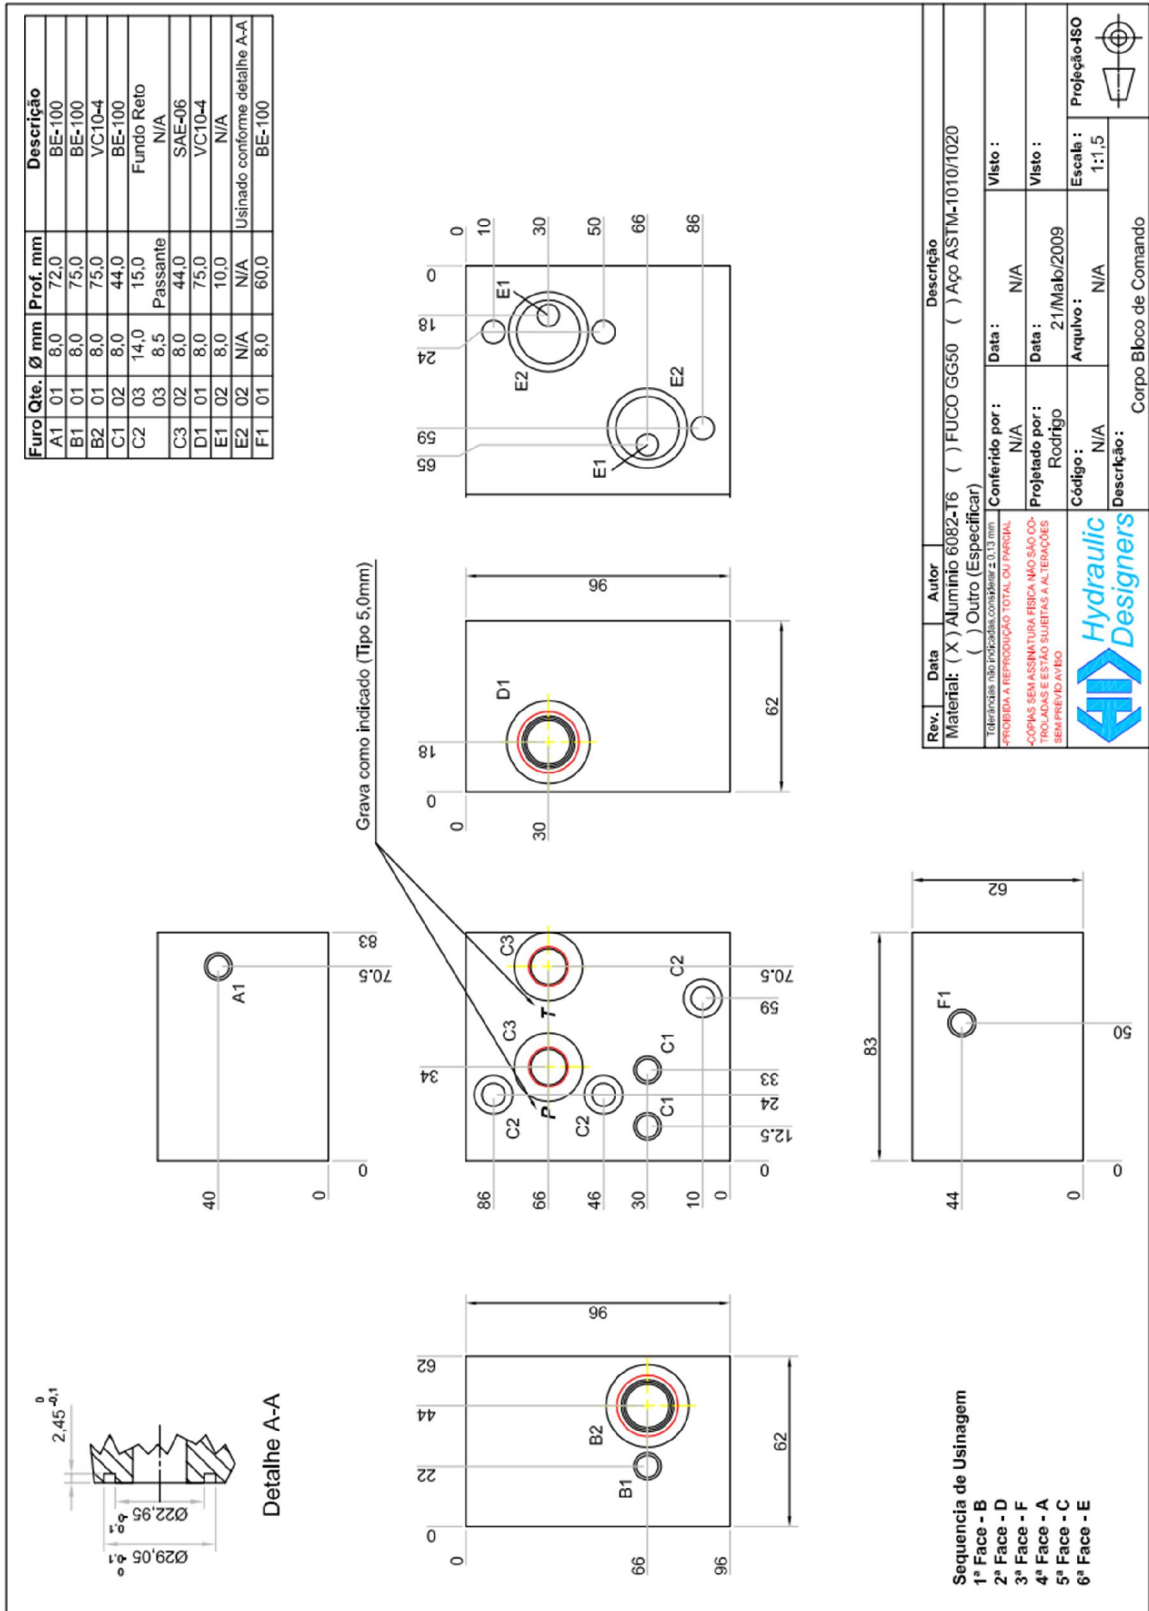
Representação esquemática para usinagem do bloco "manifold"
